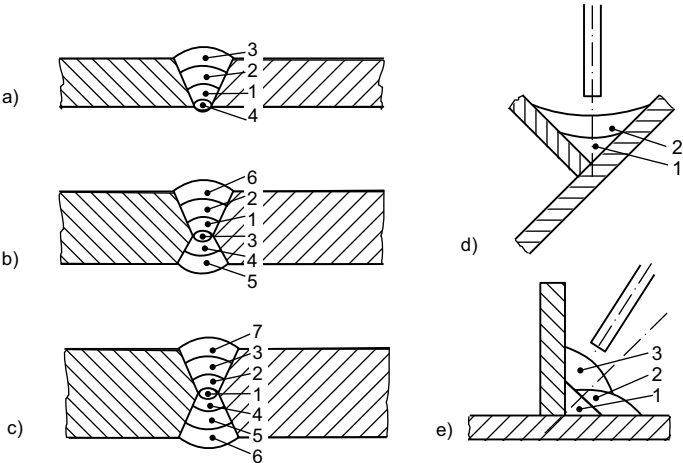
Schweißfolgen bei unterschiedlichem Nahtaufbau. a) V-Naht; b) 2/3-Doppel-V-Naht; c) Doppel-V-Naht; d) Kehlnaht Position PA; e) Kehlnaht Position PB
